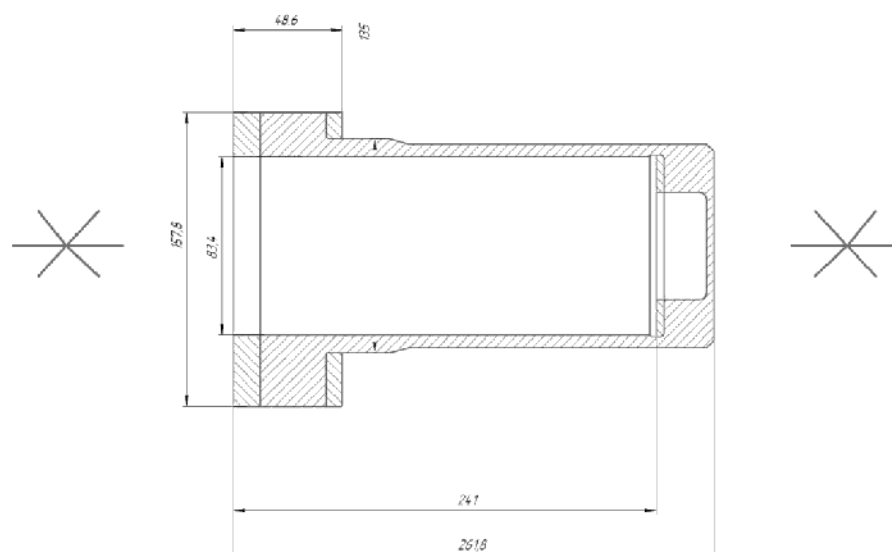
Ескіз заготовки в оболонковій формі
